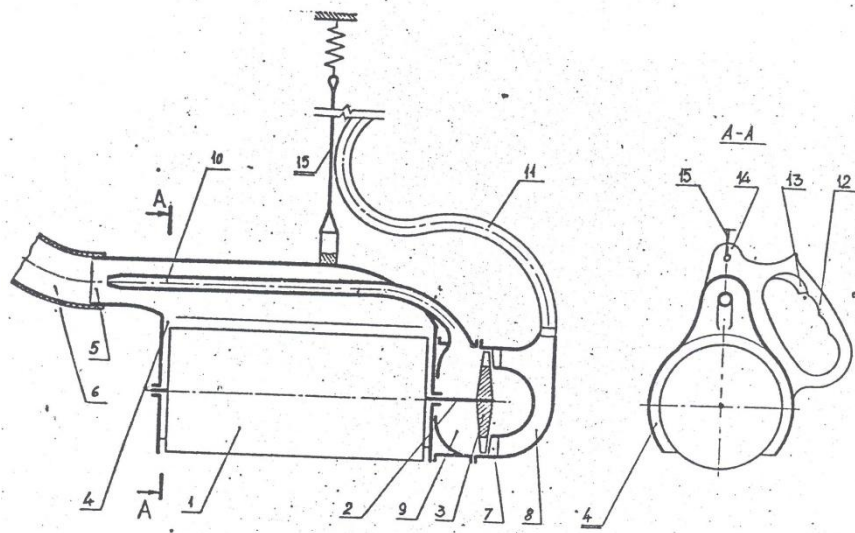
Чистильно-шлифовальный станок для валяной обуви
